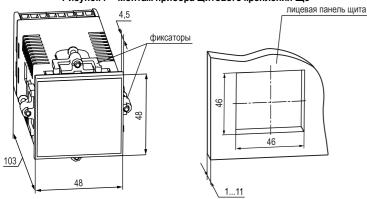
Габаритные размеры корпуса Щ5 и монтажного отверстия в щите
